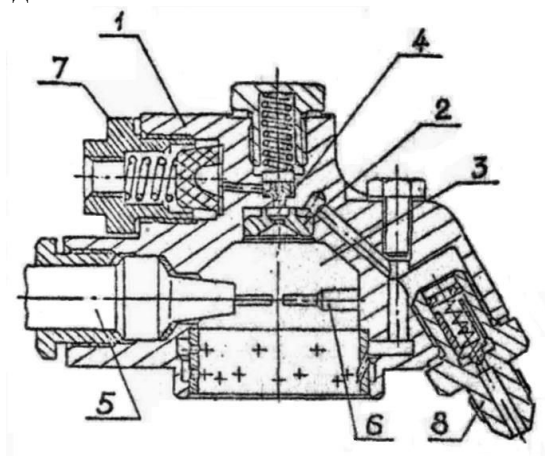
Схема устройства АФП двигателя 5ТДФ [С.216, 5]. Принятые обозначения:
